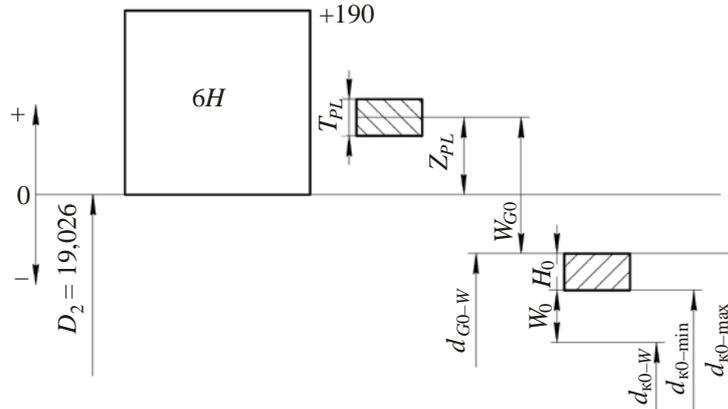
Схема расположения допусков калибров для контроля среднего диаметра гайки:
